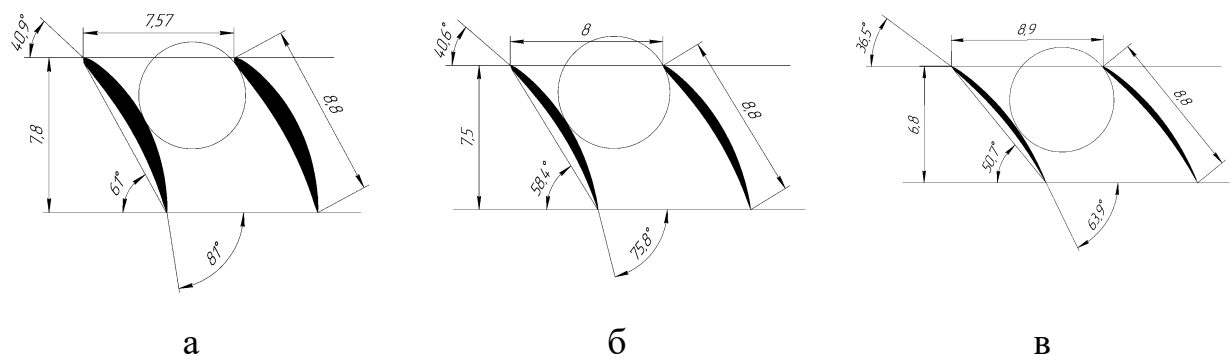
Профіль ґратки I ступеня компресора ГТД у кореновому (а), середньому (б) і периферійному (в) перерізах робочої лопатки
